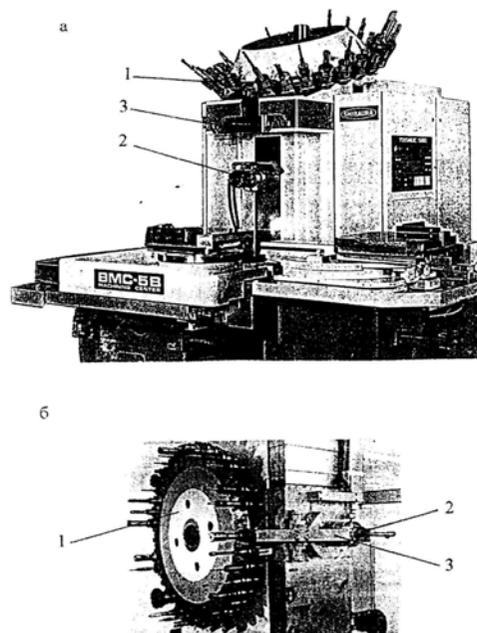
Конструктивное исполнение инструментальных магазинов барабанного типа в обрабатывающих центрах:
